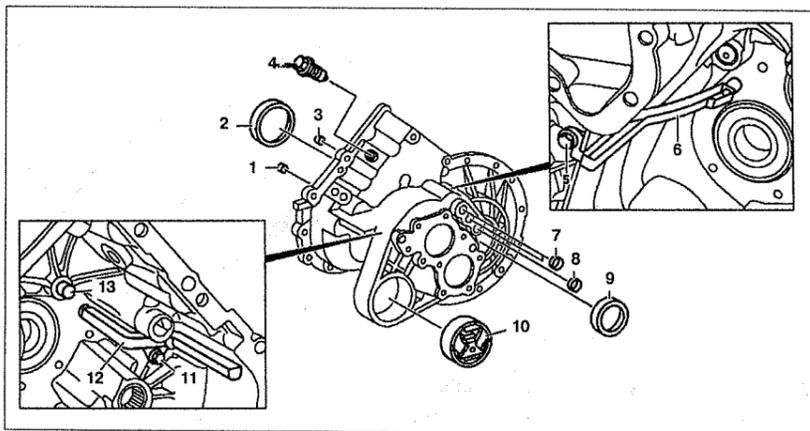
Корпус коробки передач (автомобили с двигателями 111.948 и 601.970): 1. Игольчатый подшипник вала задней передачи, 2. Наружное кольцо конического роликового подшипника, 3. Втулка подшипника рычага переключения передач, 4. Блокировочный палец, 5, 11. Болт, 6, 12. Масляный канал, 7, 8. Крышка рычага переключения передач, 9. Вращающийся сальник, 10. Опора, 13. Направляющий болт замка блокировки переключения передач.
